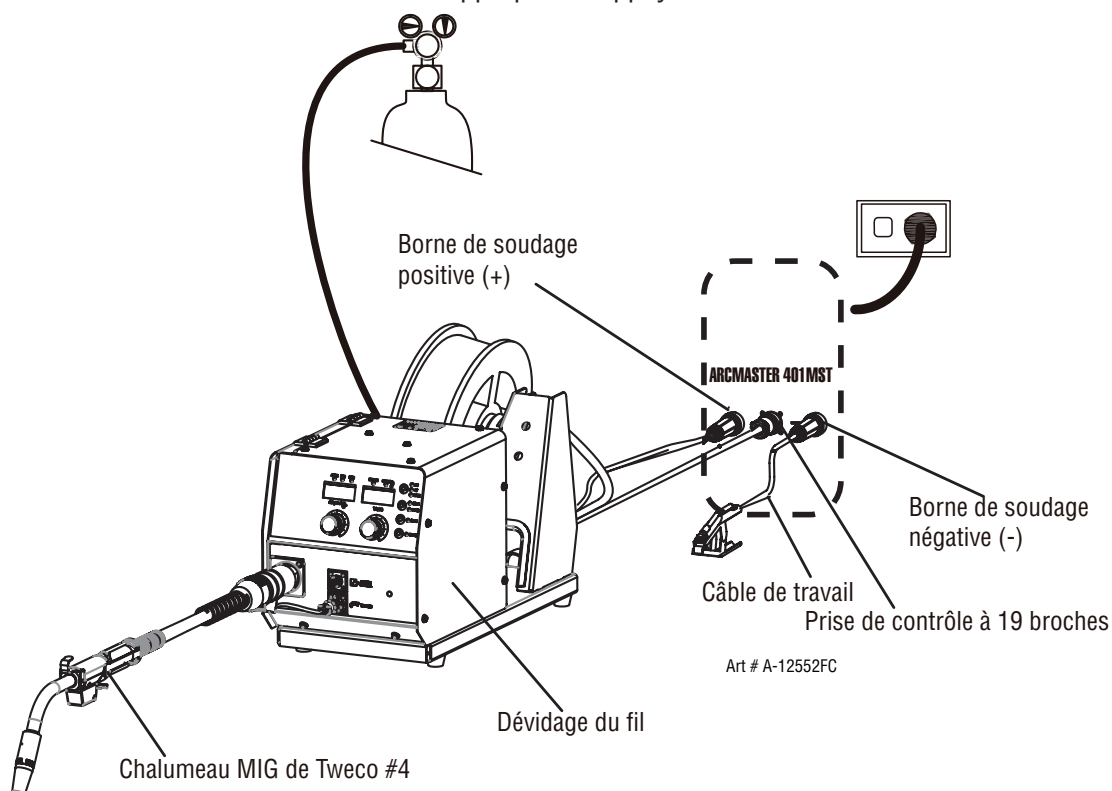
Réglage pour soudure MIG (GMAW) avec fil MIG sous protection gazeuse
